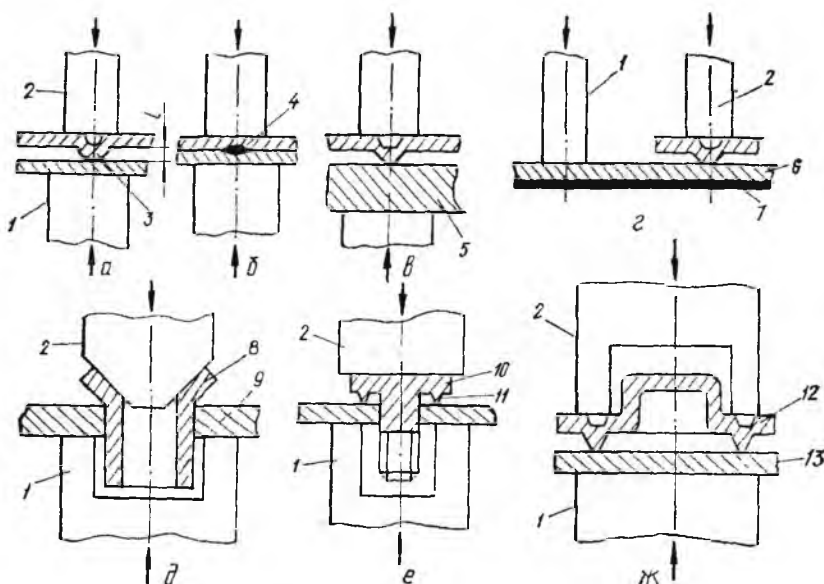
Схемы рельефно-точечной и рельефно-контурной конденсаторной сварки.
